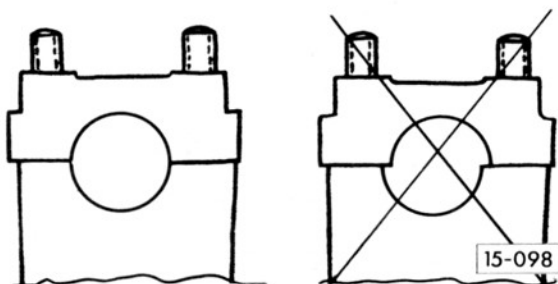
Einbaulage Lagerdeckel-Nockenwelle
